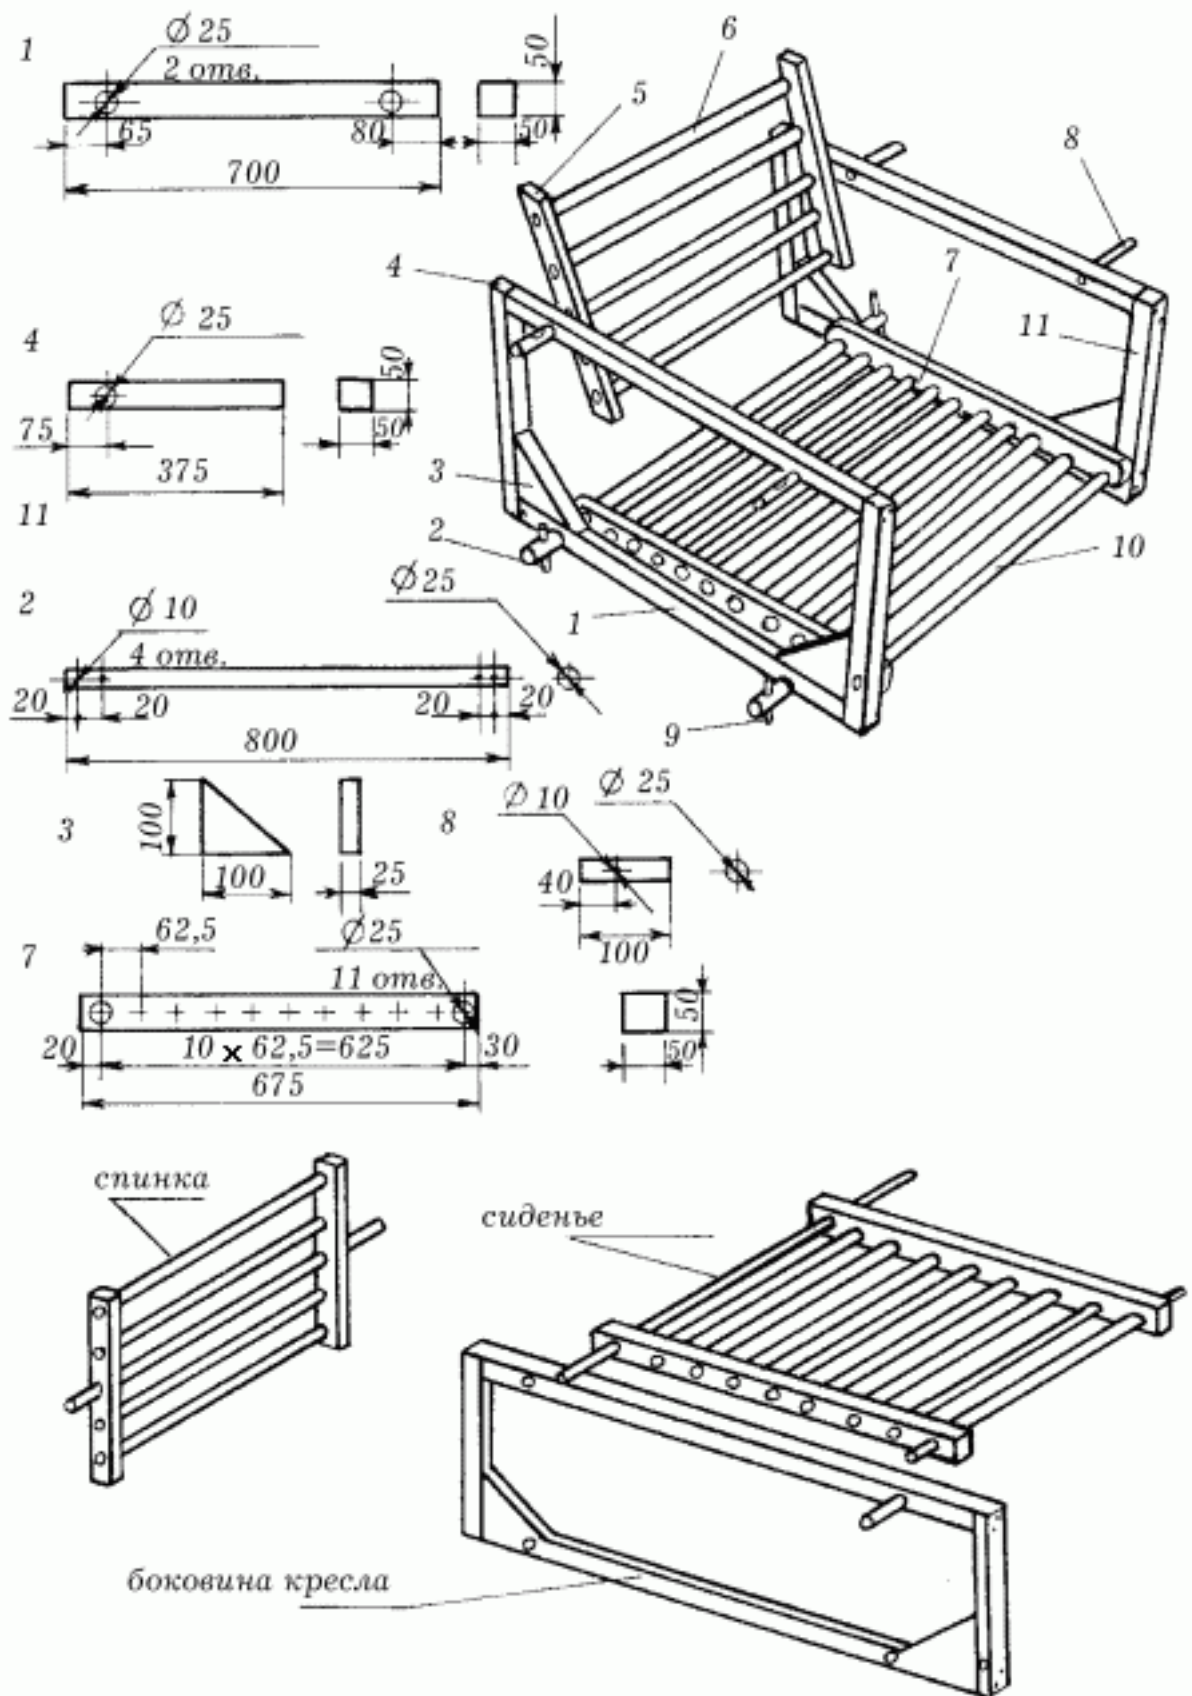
Кресло-качели: 1 – горизонтальный элемент боковины; 2 – стержень соединительный; 3 – угольник усиливающий; 4, 11 – вертикальные элементы боковины; 5 – элемент каркаса сиденья; 6 – элемент решетки спинки и сиденья; 7 – элемент каркаса сиденья; 8 – направляющая шнура-подвески; 9 – штырь; 10 – фиксатор сиденья.
